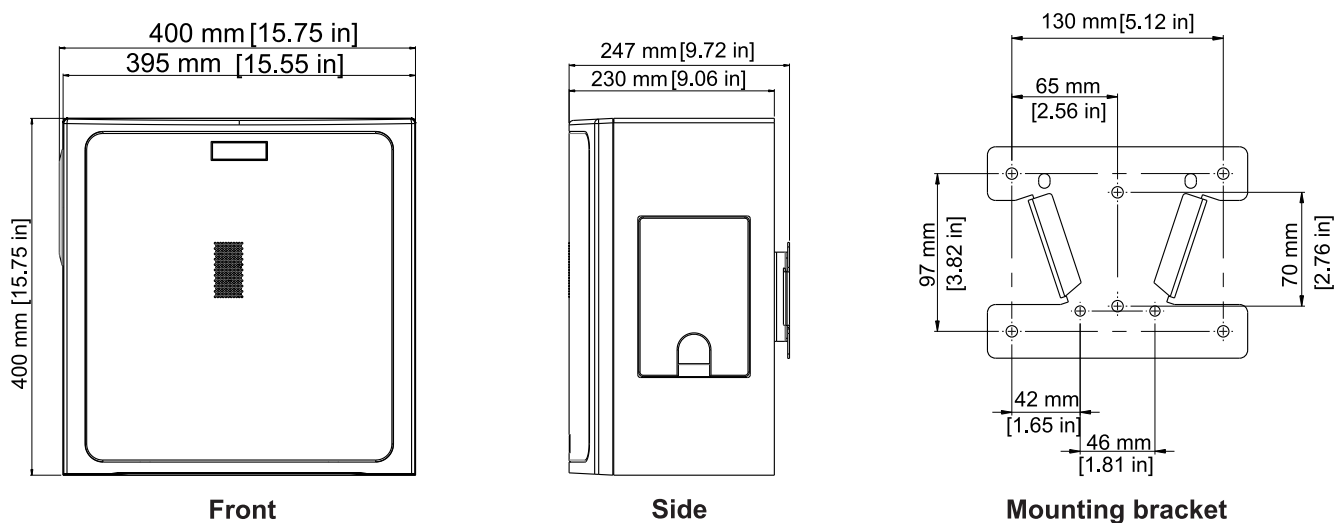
Dimensiones LB6-SW100-Dy soporte de montaje
